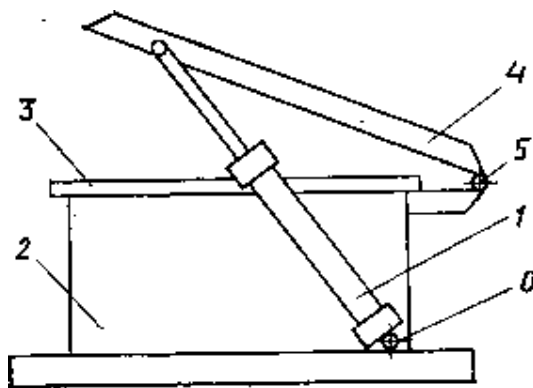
Затискна рама з єдиними циліндрами для її підйому та затиску заготовки
